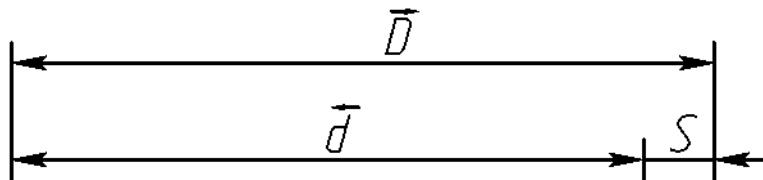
Размерная цепь для сборочного узла двигателя автомобиля
